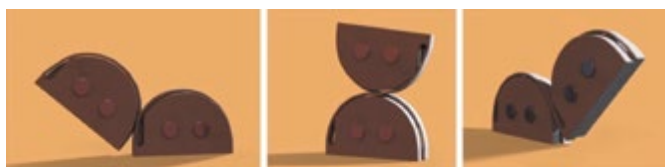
Внешний вид цилиндрического шарнира двойного действия (D-CORE) в различных стадиях
